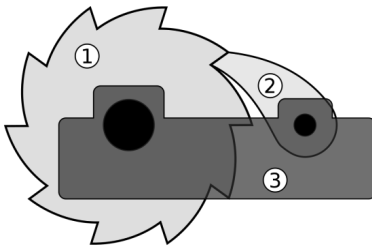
Храповий механізм: 1 – зубчасте колесо; 2 – заскочка; 3 – станина
